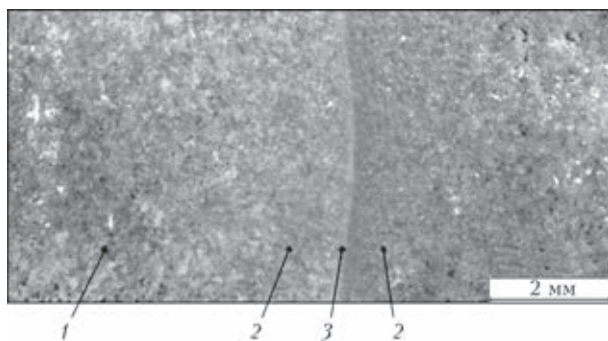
Макроструктура сварного соединения заготовки из спеченного титана BT1-0, полученной сваркой трением: 1 — основной металл; 2 — околошовная зона; 3 — шов
